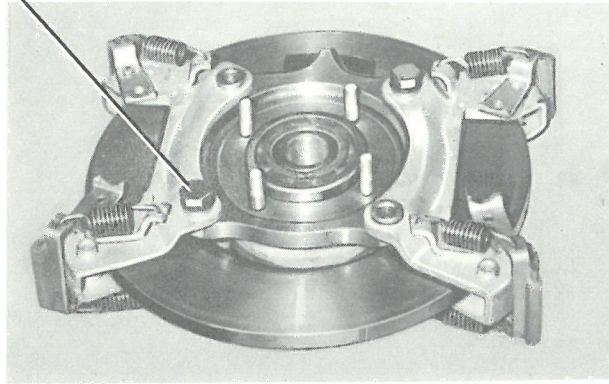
Vue de l'ensemble frein-disque après dépose
